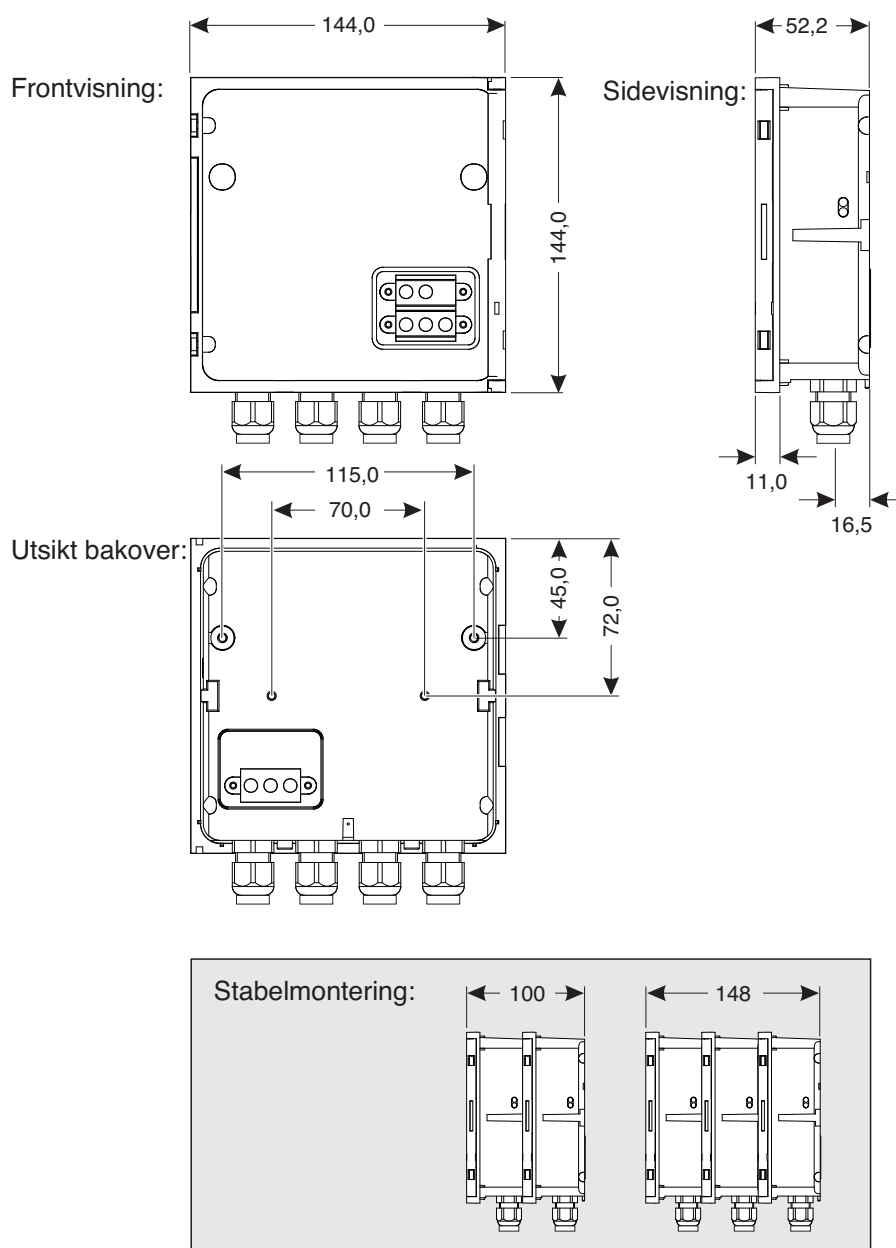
Dimensjonstegning av MIQ-modul (dimensjoner i mm)
